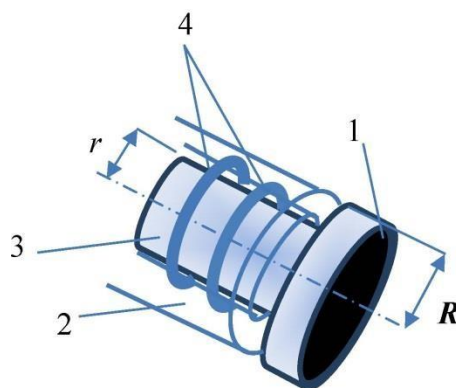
Конструкція обертаючихся навколо свого центру різців типу PDC:
